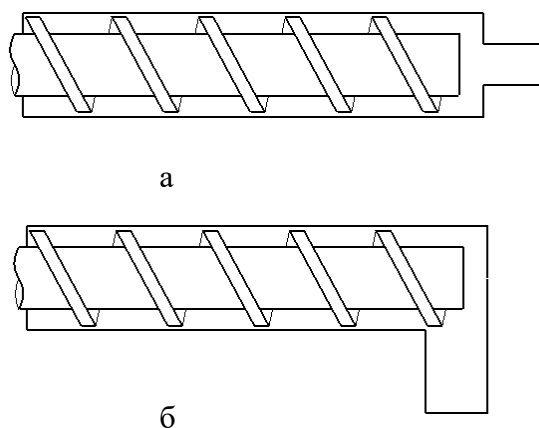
Варианты расположения мундштуков фрезформовочной машины:
